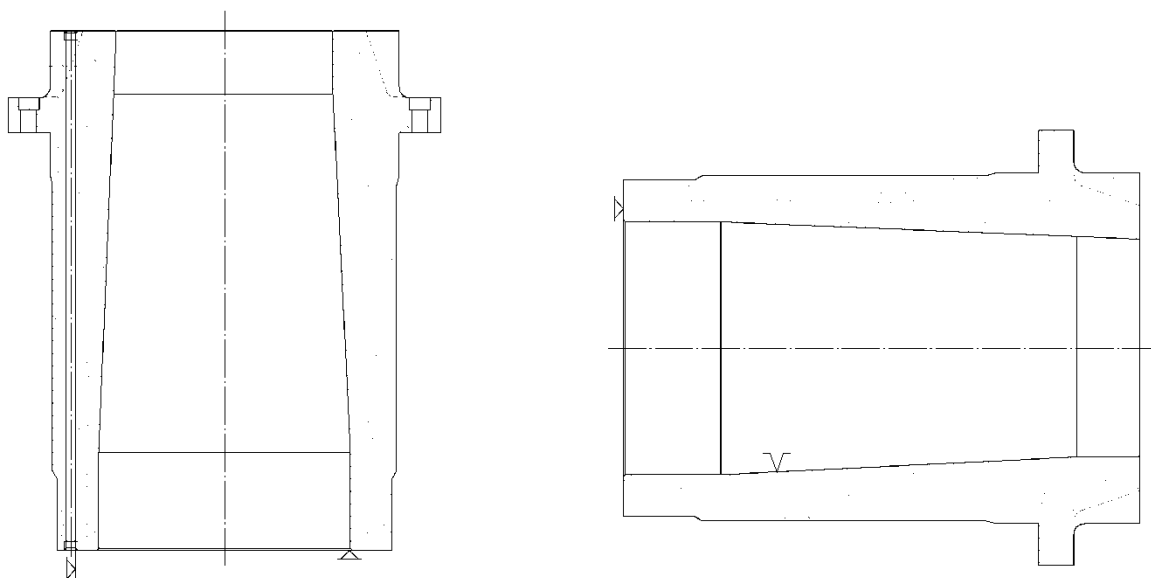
Умовні схеми закріплення деталі при обробці
